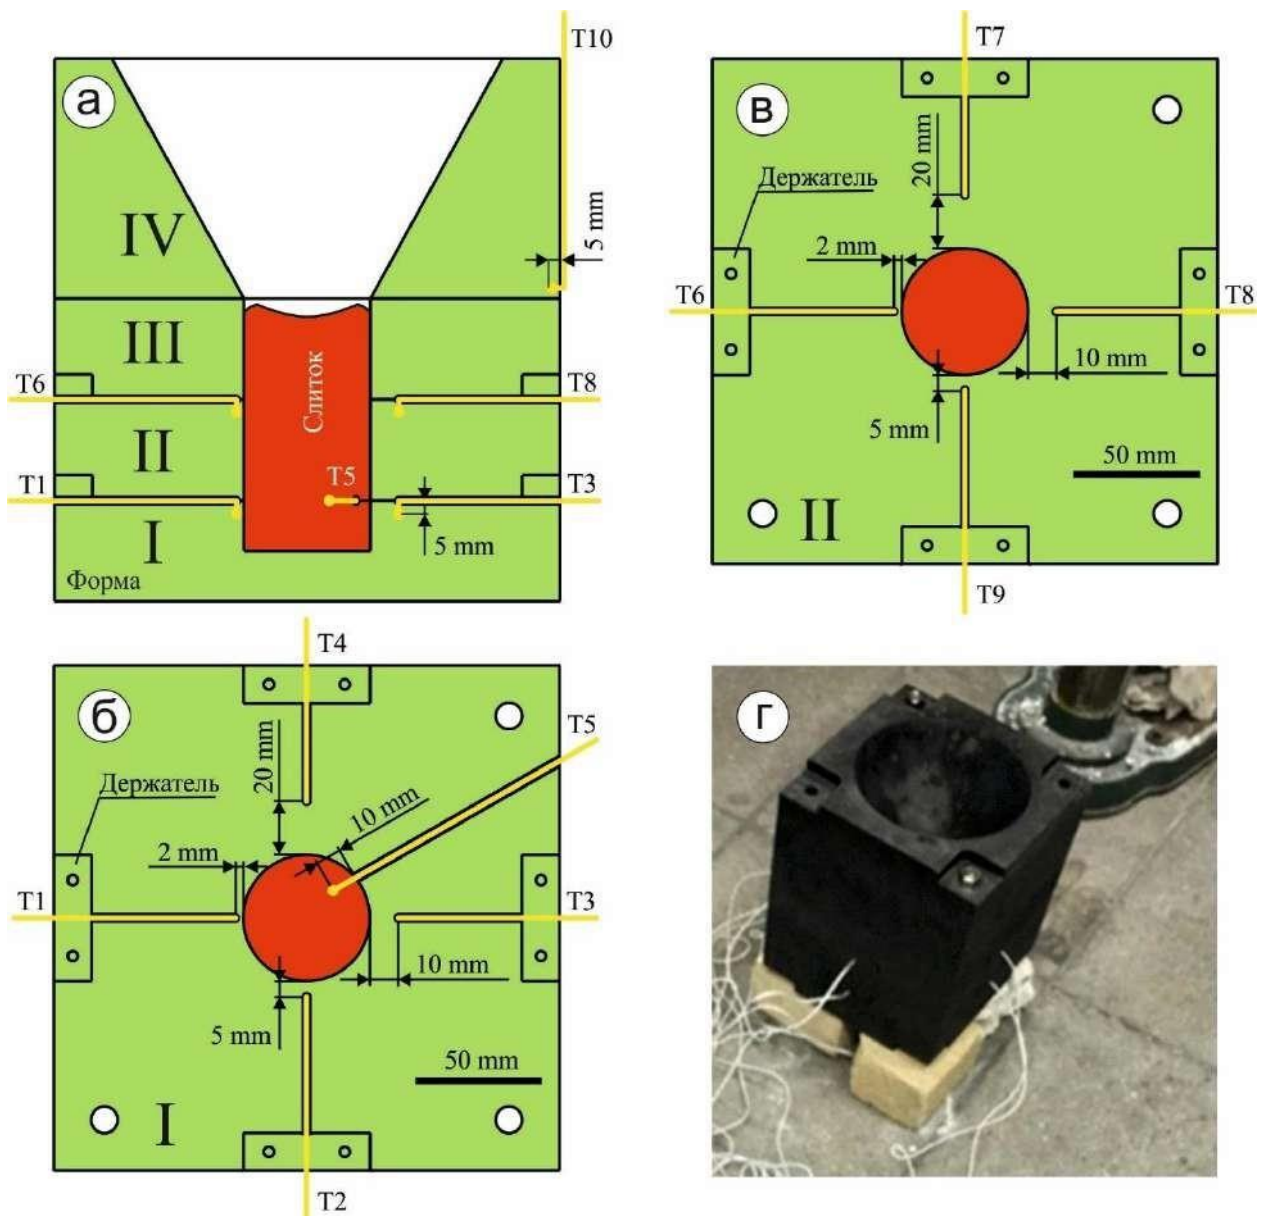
Схема розташування термопар у формі з графіту номер 1; а) - форма в розрізі; б) - вид на частину форми I; в) - вид на частину форми II; г) - загальний вигляд форми в зборі зі встановленими термопарами
